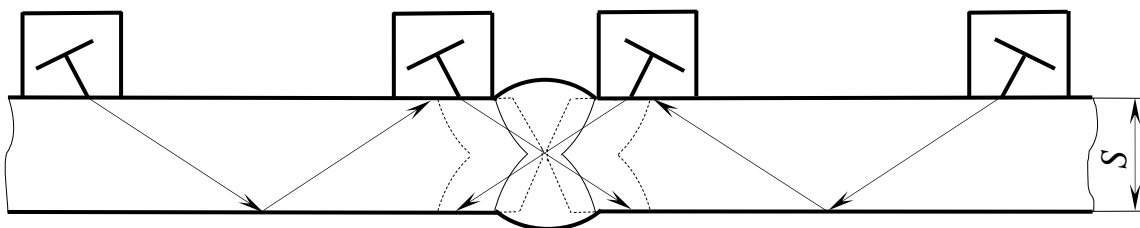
Схема контроля стыковых сварных соединений, выполненных двухсторонней сваркой
